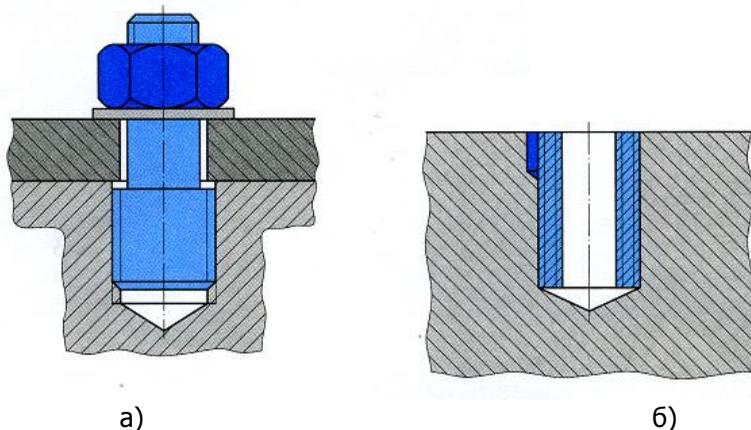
Схемы восстановления резьбовых соединений:
